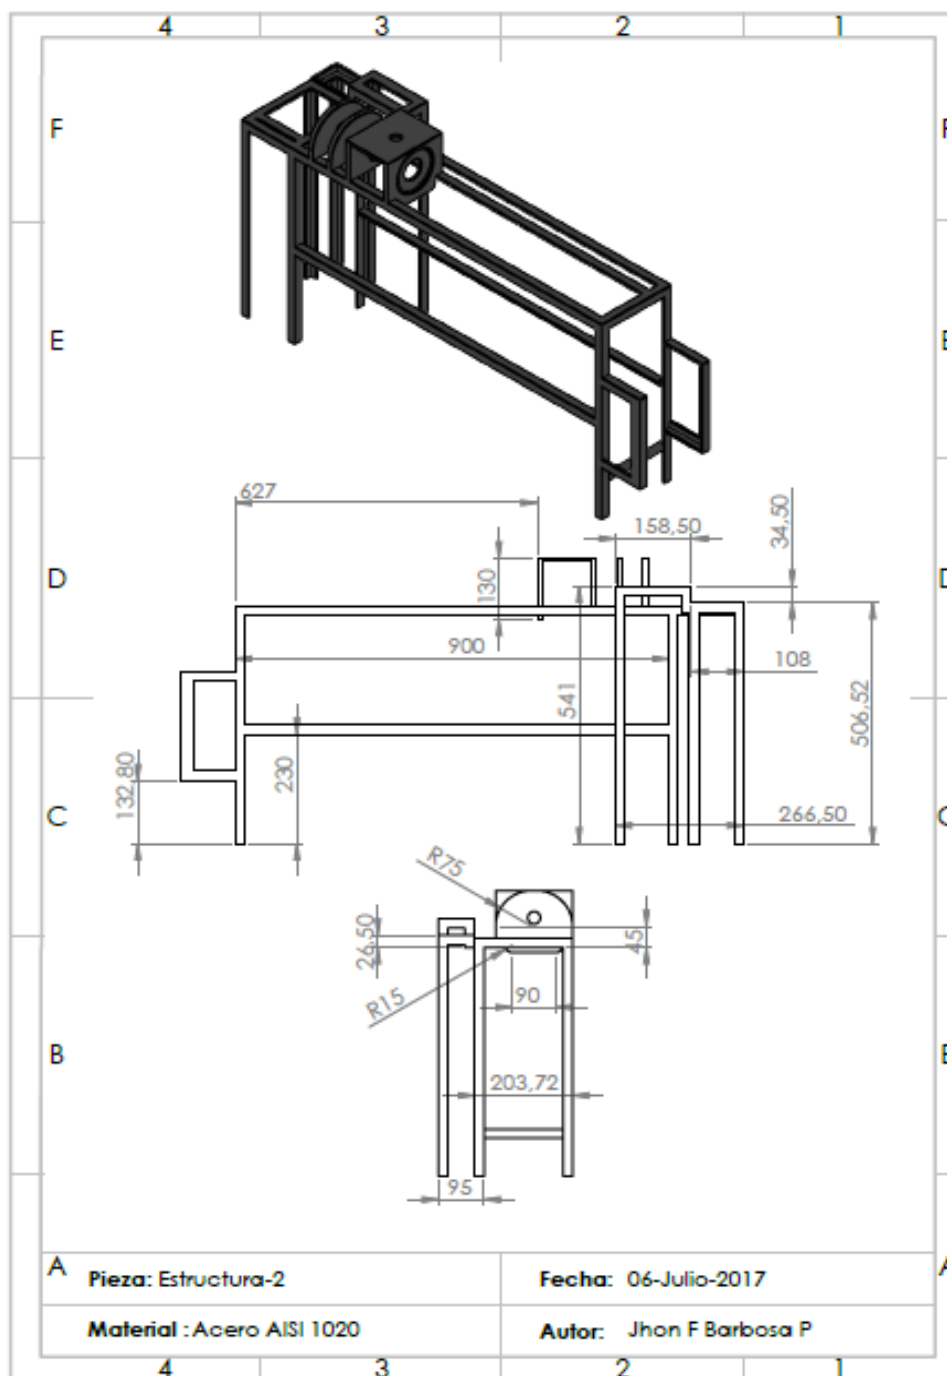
Plano 1 de la estructura de la máquina extrusora.
